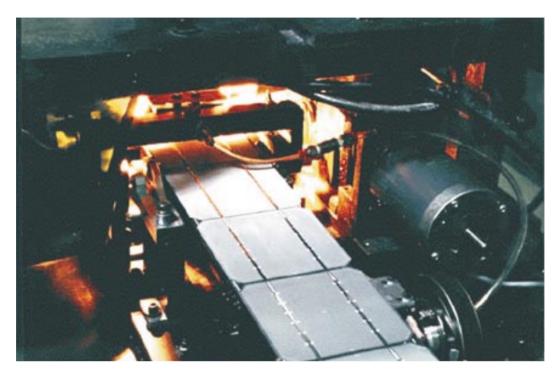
Proceso de soldadura de la rejilla metálica durante el ensamblaje del panel.
